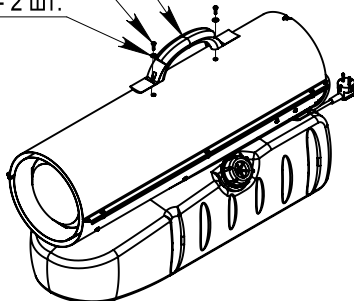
Установка ручки для переноса KHD-20 и KHD-30
